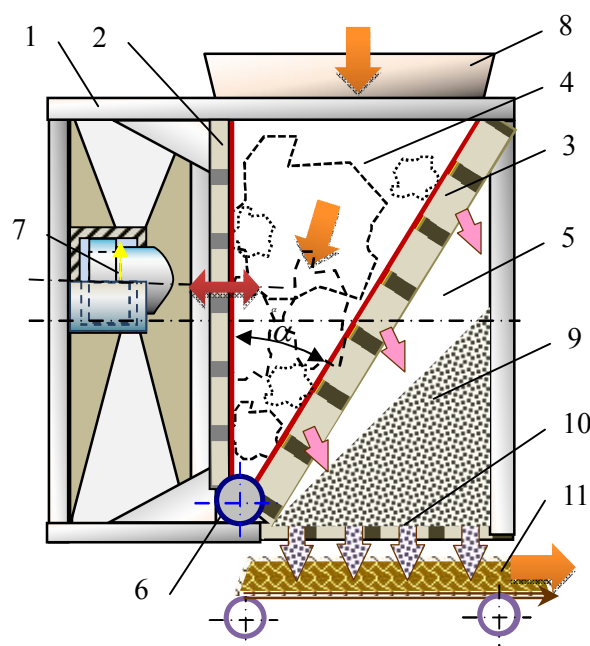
Схема ударной щековой дробилки с гидроприводом и дробящими плитами колосниковой конструкции
